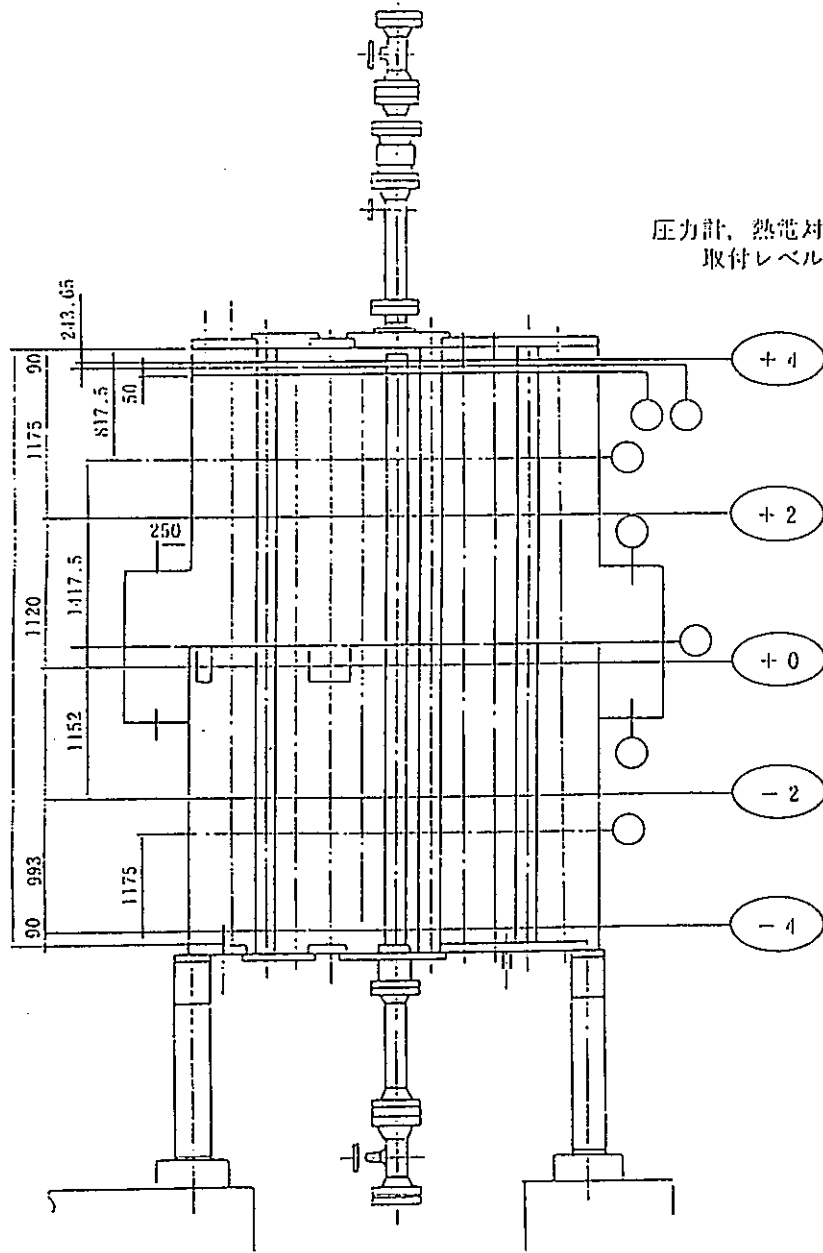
周辺カランドリア管計測器配置図 (PTC-6)
